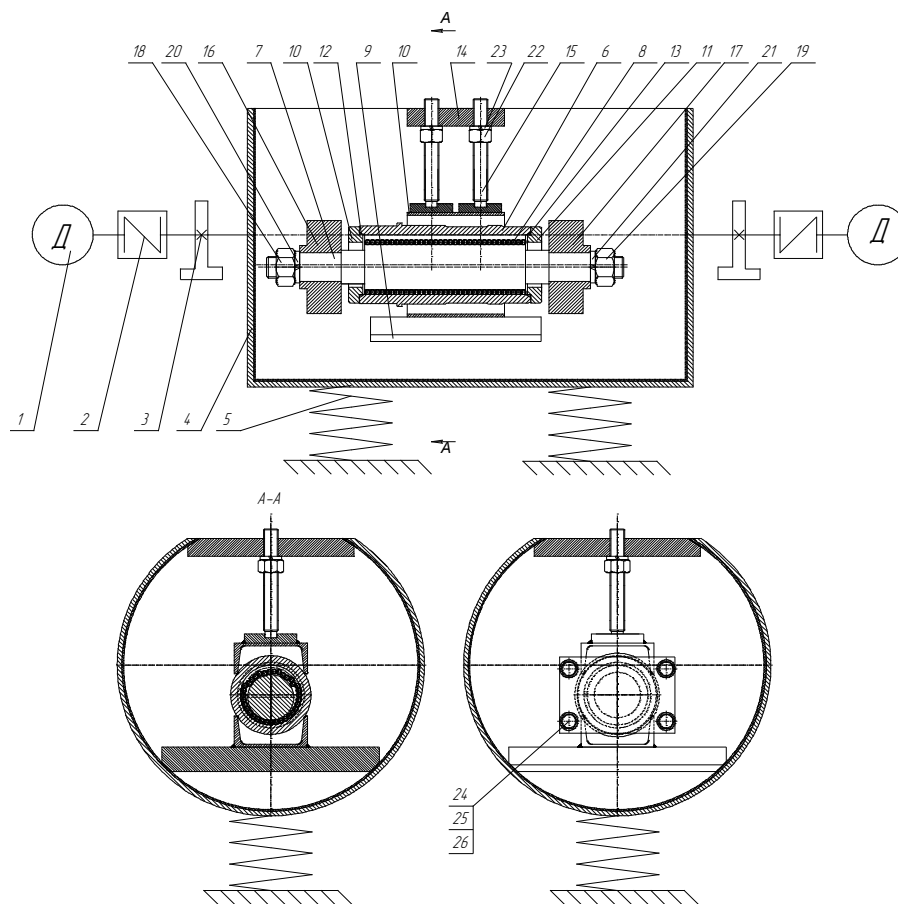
Принципова схема технологічного обладнання для вібраційного оброблення
